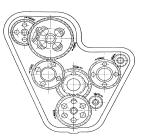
Схема распределительных шестерен двигателя Fig. 5. Engine Timing Gears
